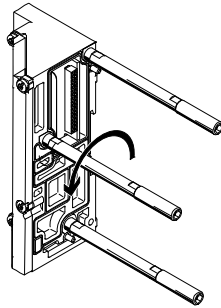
Entfernen der Gewindestangen von der linken Endplatte
